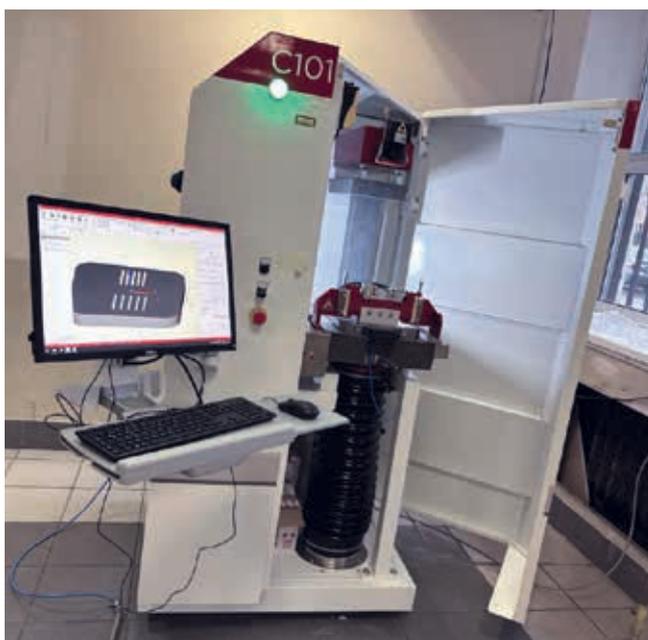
Внешний вид аддитивной установки C101 EASY LAB 3D Ceram (Франция)
